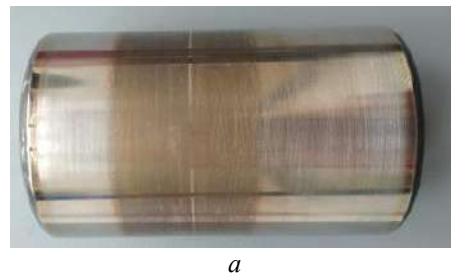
Детали подшипников с дефектами, которые являются основными причинами отказов:
